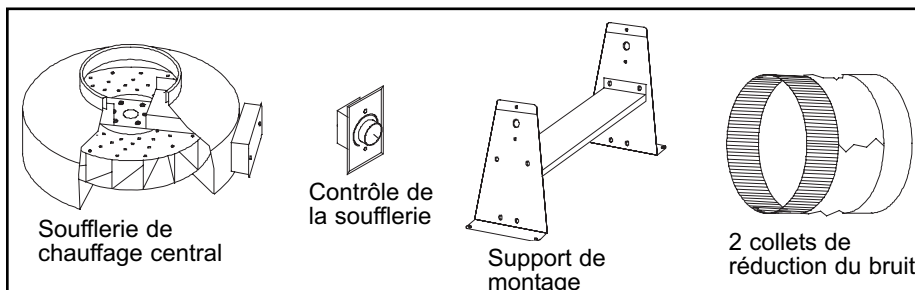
Trousse de la soufflerie du chauffage central (FDHB6)
